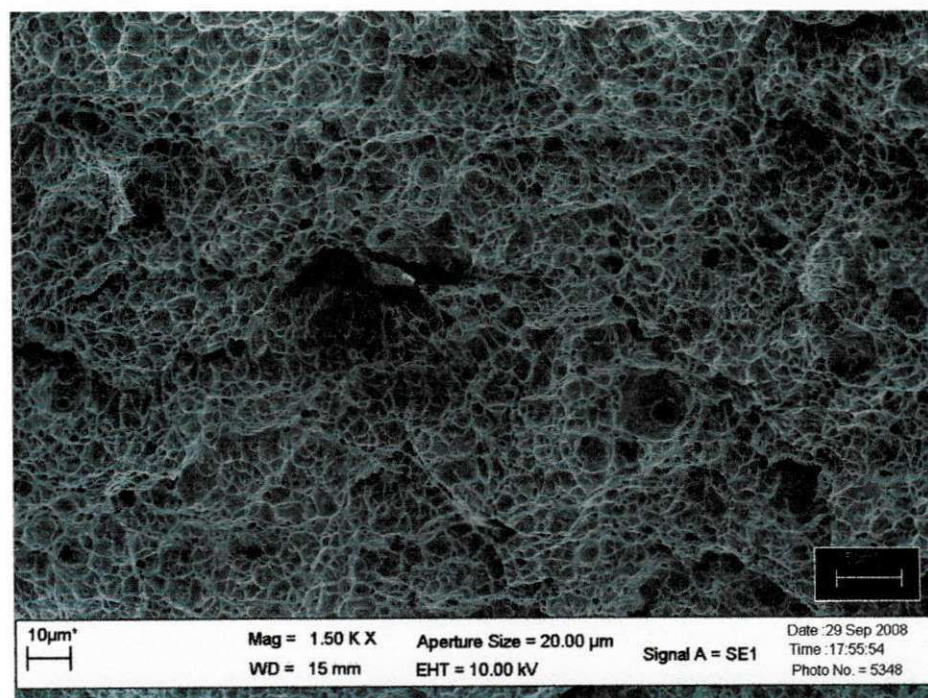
MEV na região de fratura (entalhe posicionado no passe de enchimento), M1, 1500X.
